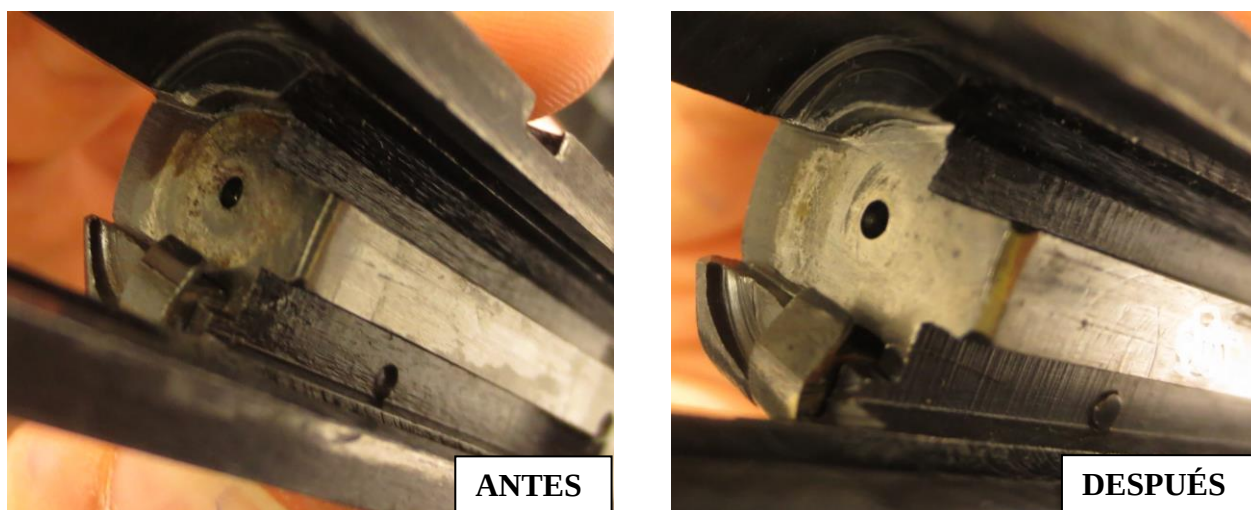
Vista de frontal de cierre de la pistola Star antes y después de la limpieza
